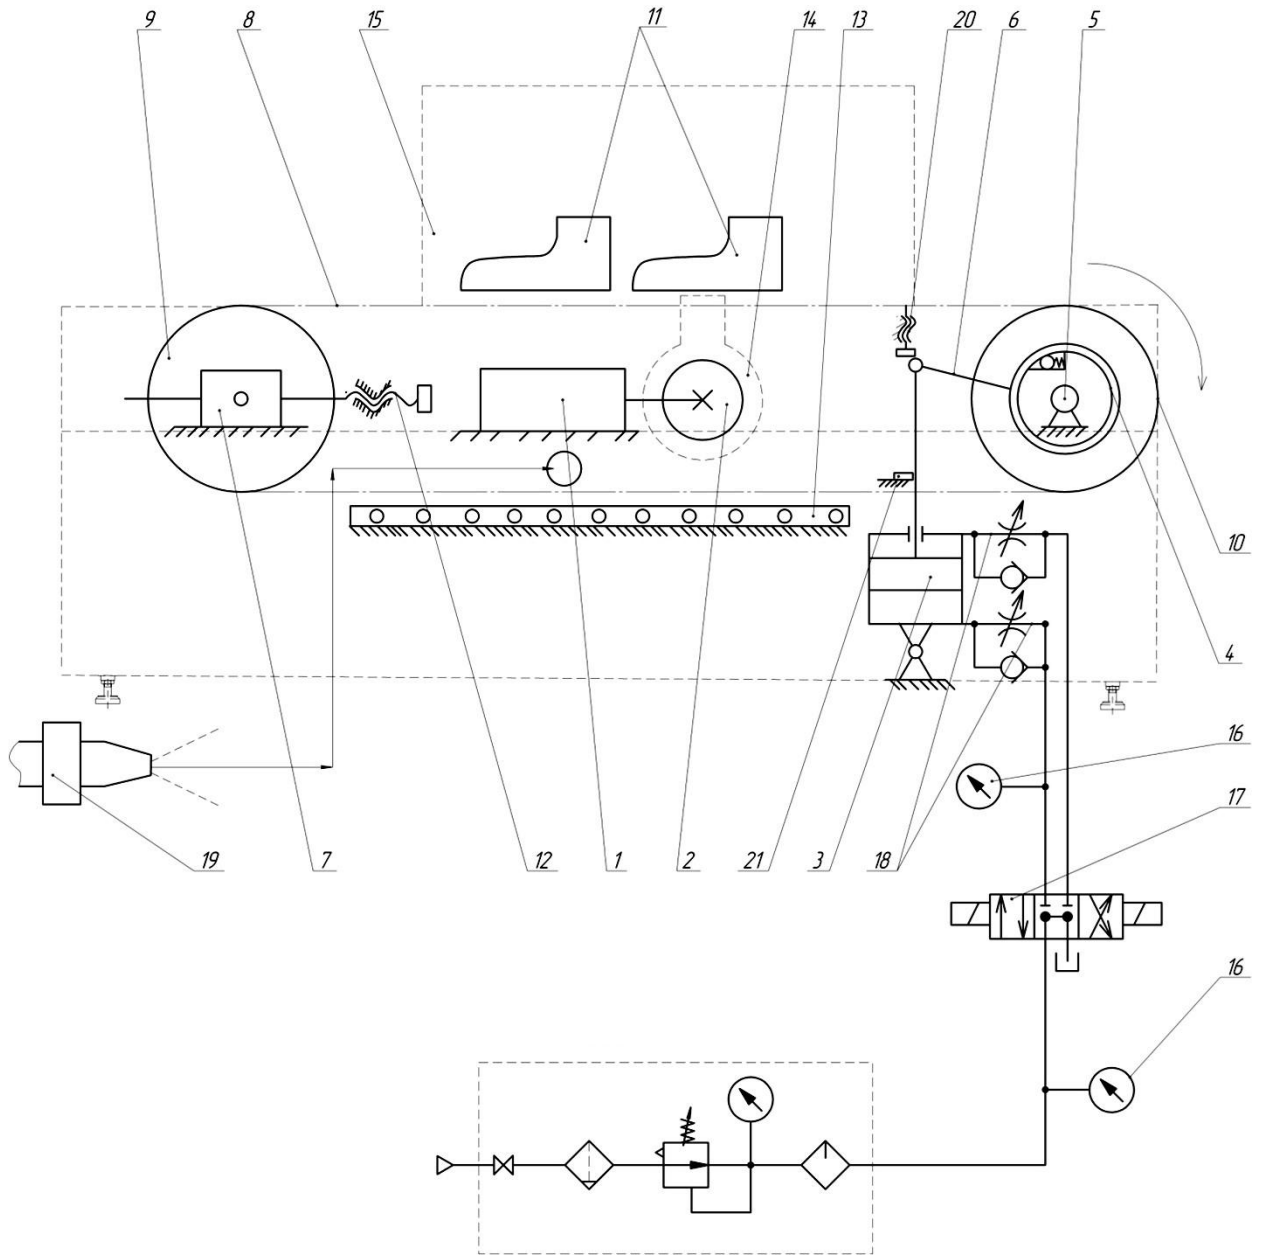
Пневмокінематична схема установки для термозволоження заготовок верху взуття
